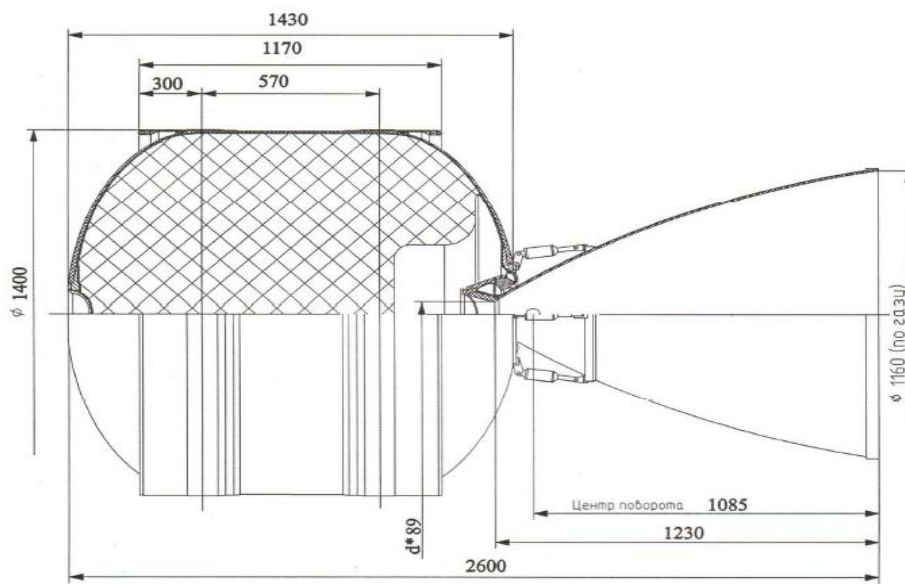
Габаритный чертеж второй ступени с РДТТ.
